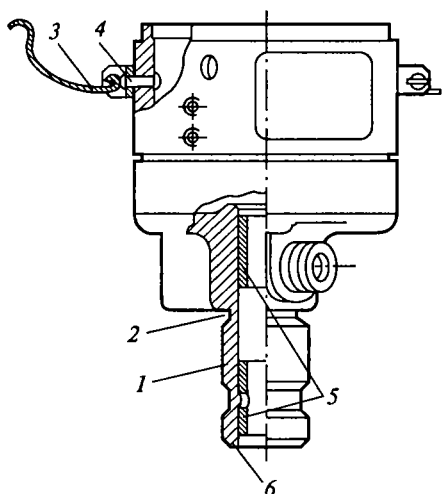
Схема расположения дефектов корпуса распределителя классической системы зажигания:
